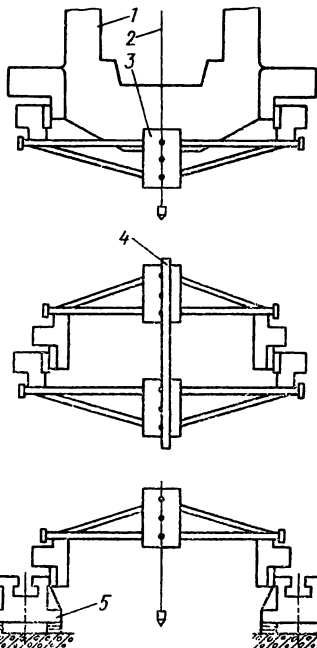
Схема установки плитовина: 1 — станина рабочей клетки; 2 — осевая струна; 3 — регулируемый шаблон; 4 — линейка; 5 — плитовина
